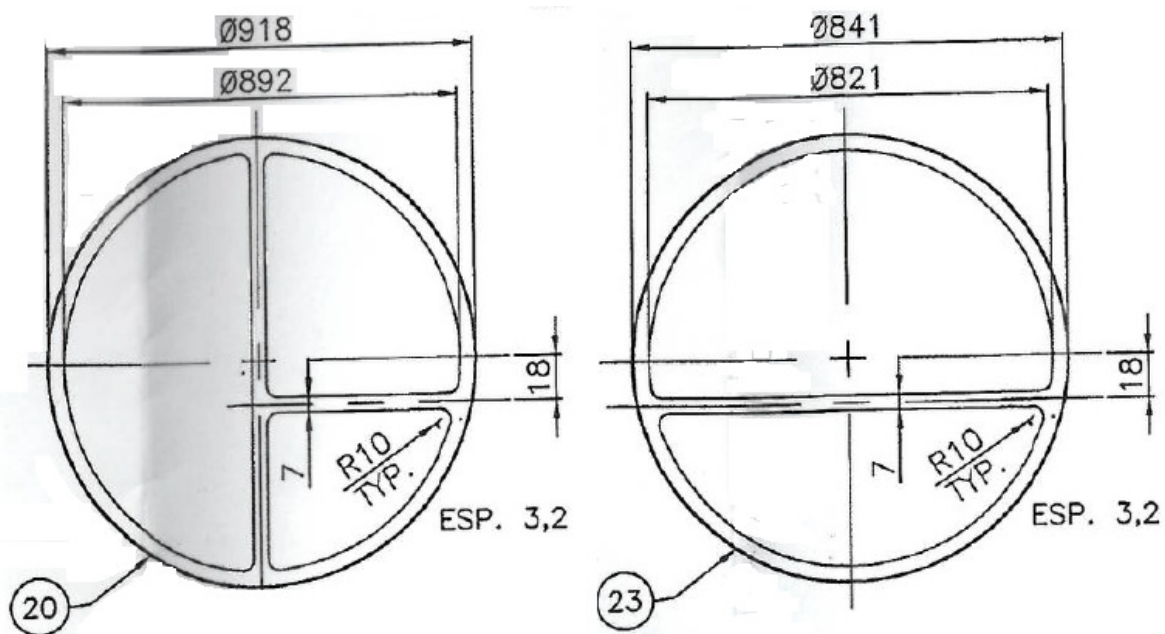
Plano de empaquetaduras enchaquetadas del 3E – 3209 / 3E – 3209 A
